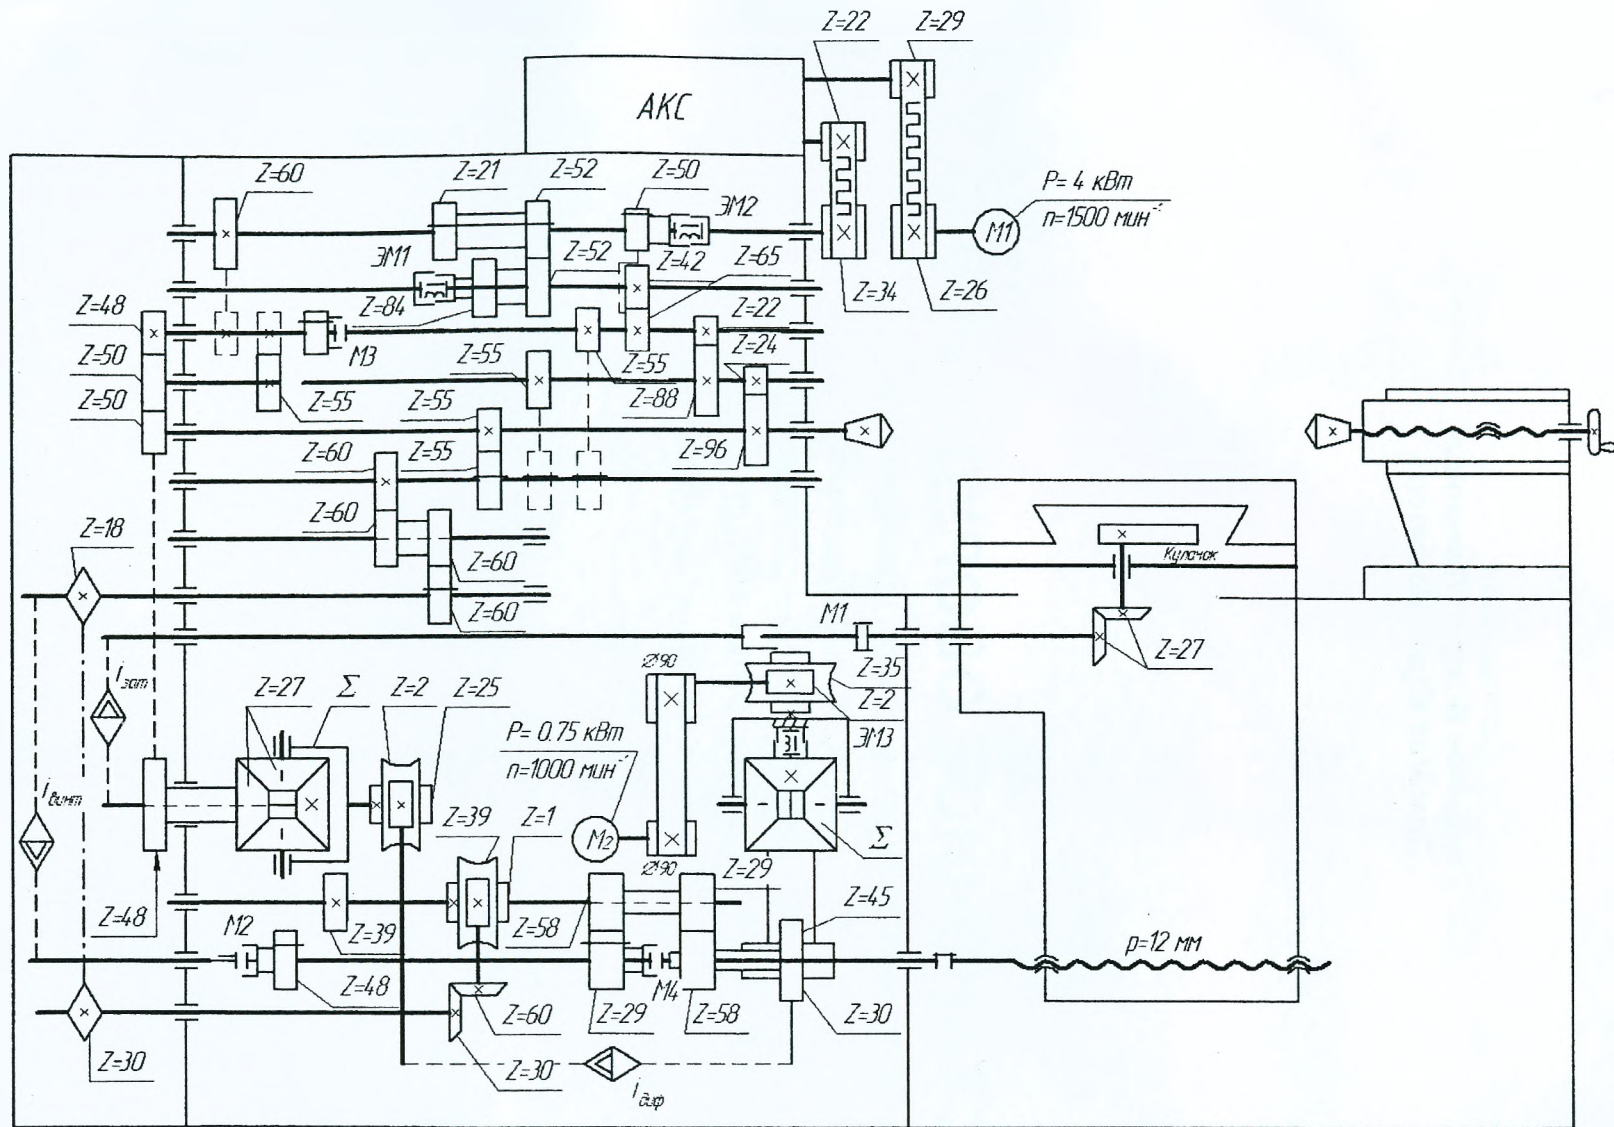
Кинематическая схема токарно-затыловочного станка мод.1E811
